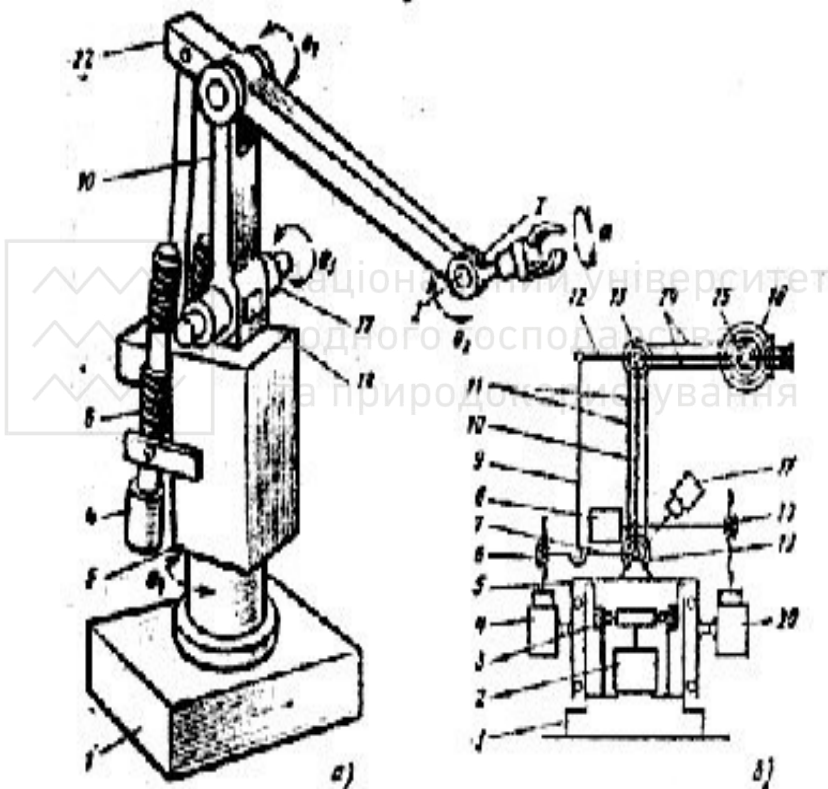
Промисловий робот: а) компоновка; б) кінематична схема: 1-основа; 2,4,17,20-електродвигуни з редукторами; 3-хвильова передача; 6,18-кулькові гвинтові пари; 5-поворотний корпус; 7-тяга; 8-зрівноважуючий вантаж; 9,10,12-ланки руки; 11-14-тяги; 13,15,19-кривошипи; 16-кінцева передача.
